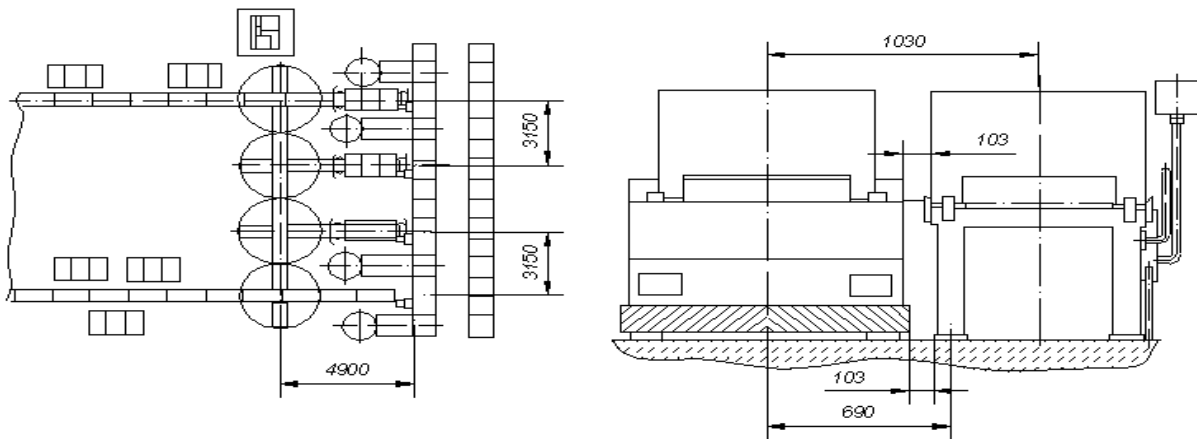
Схема планировки и общий вид АТСС на базе транспортного робота РБТ-1
